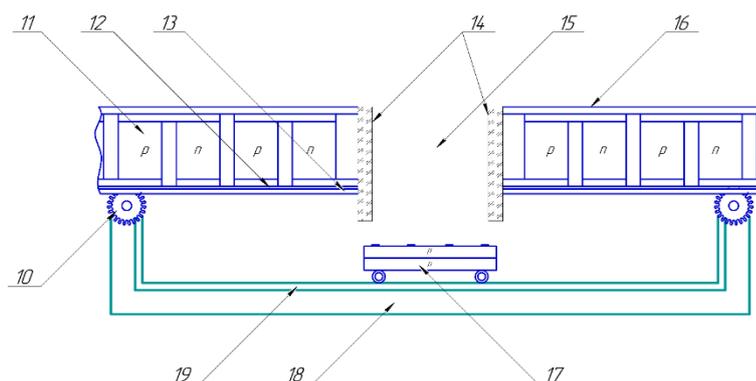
Конструктивная схема защитного блока с подвижной щелью
